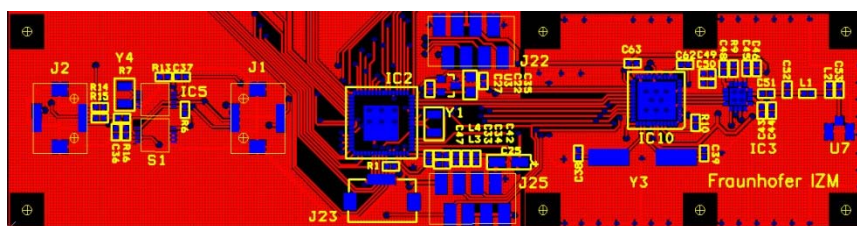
Layout für die Sensorknoten-Baugruppe
